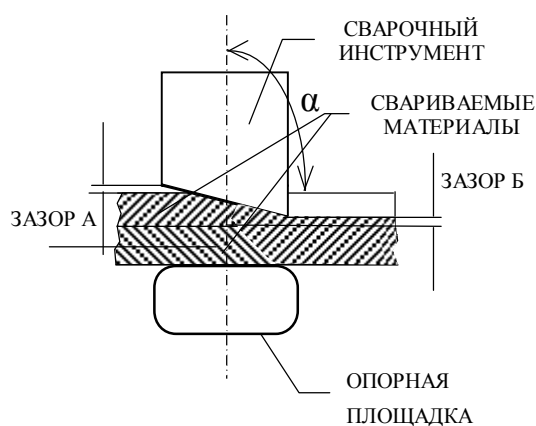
Схема непрерывной ультразвуковой сварки
